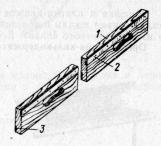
1 — рейка; 2 — пластина верхняя; 3 — пластина нижняя
